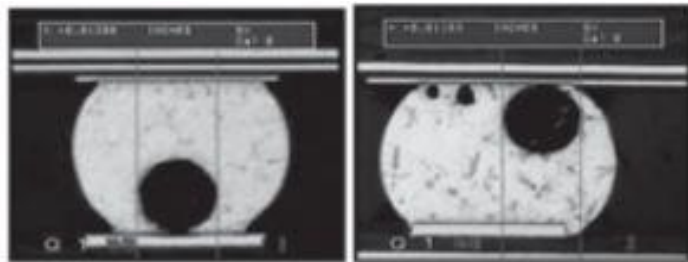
Rozmístění voidů v pájeném spoji [11].
